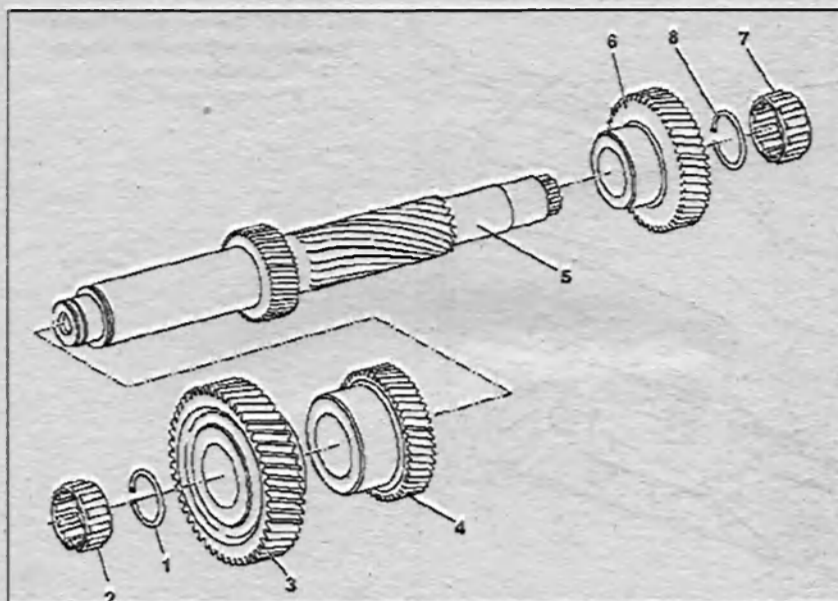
Разборка и сборка промежуточного вала МКПП 711.605:
